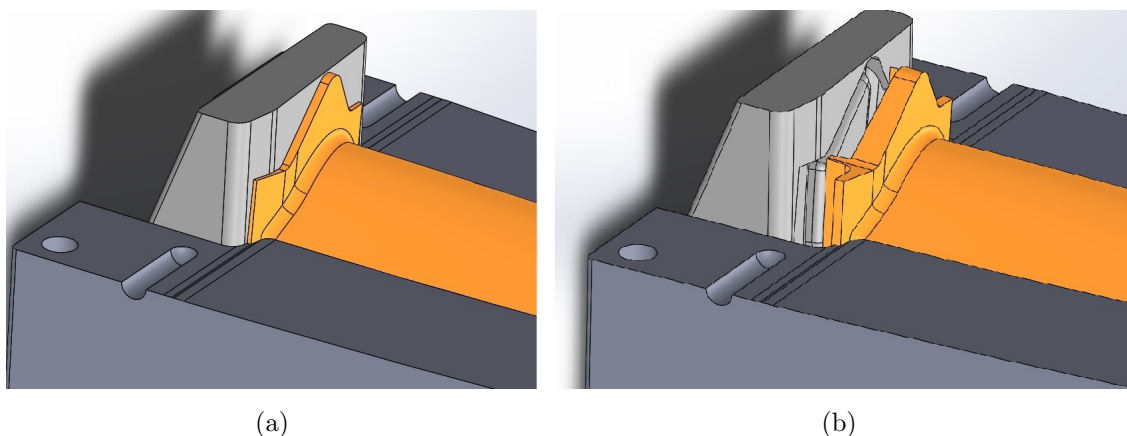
Posições do movimento, (a) posição posterior após abertura do molde, (b) posição anterior para a remoção da peça
